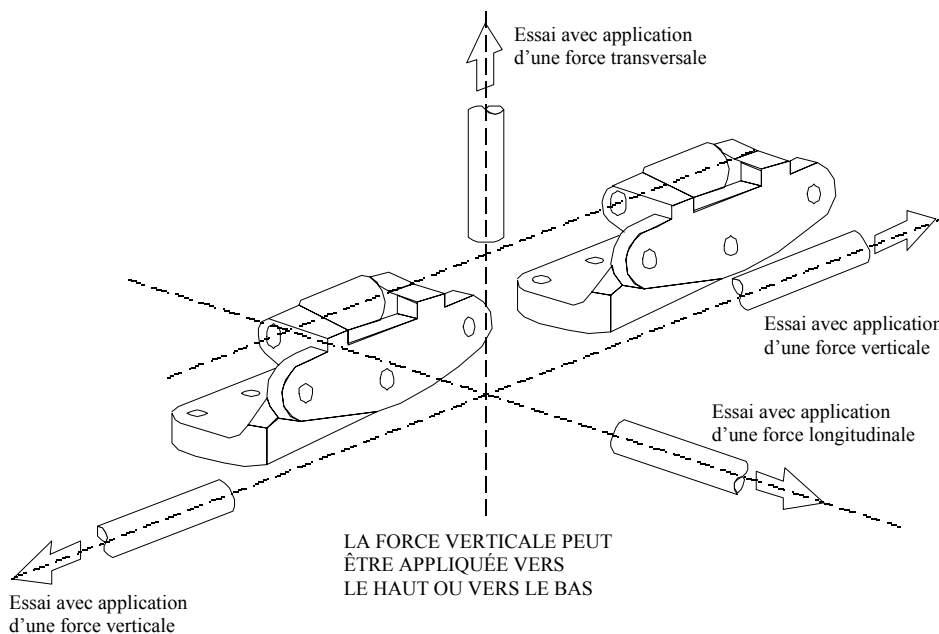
Directions d'application des forces lors des essais statiques sur les portes arrière
